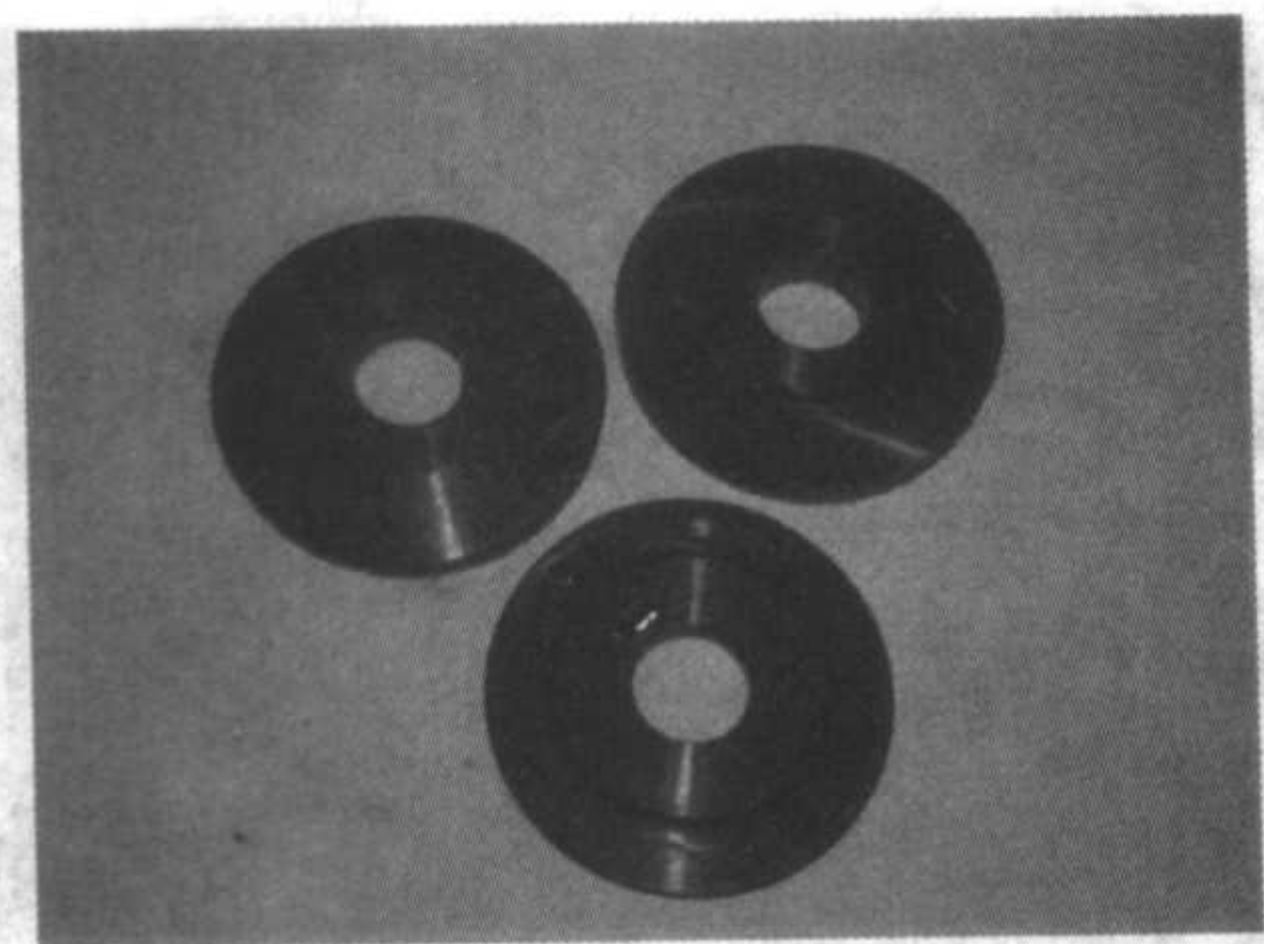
氮化硅陶瓷焊接盘
